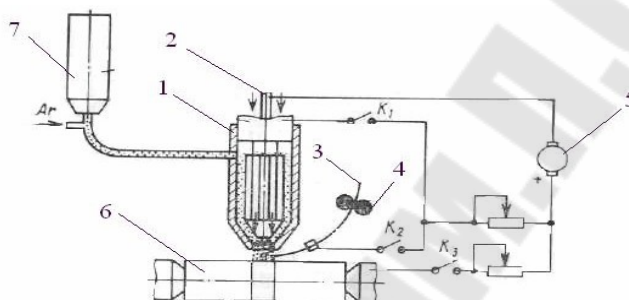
Схема установки плазменной наплавки комбинированным способом: 1 – корпус плазмотрона (анод); 2 – вольфрамовый электрод; 3 – электродная проволока; 4 – механизм подачи проволоки; 5 – источник питания; 6 – наплавляемая деталь; 7 – порошковый питатель
